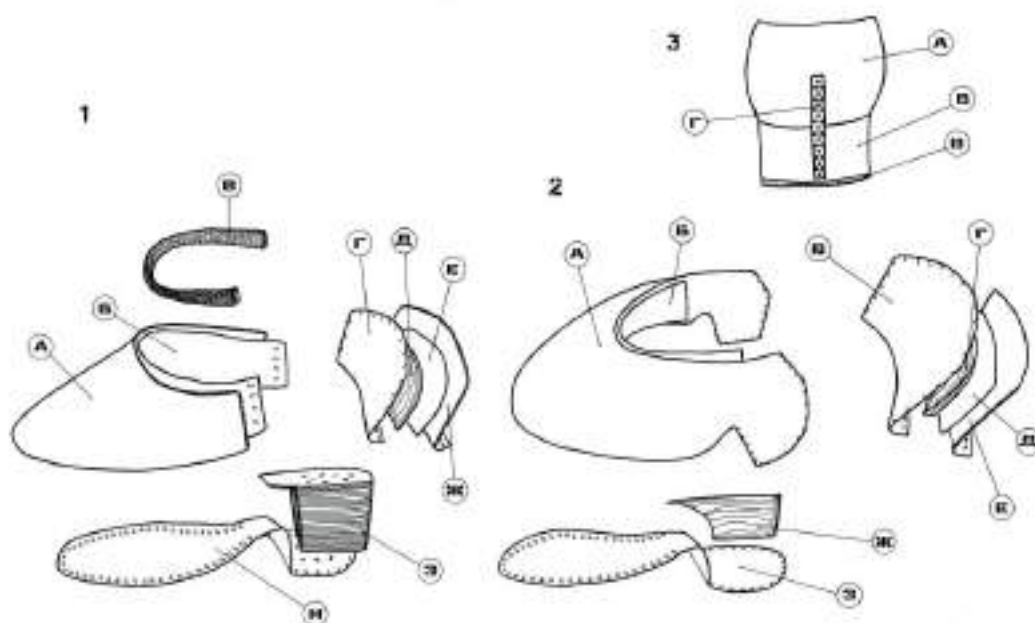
Схемы сборки башмаков. 1 – конструкция с наборным кожаным каблуком: А – головка; Б – поднаряд; В – тканая обшивка; Г – карман задника; Д – деревянный вкладыш; Е – кожаная прокладка; Ж – задник; З – наборный каблук; И – подошва. 2 – конструкция с деревянным каблуком: А – головка; Б – поднаряд; В – карман задника; Г – берестяной вкладыш; Д – кожаная прокладка; Е – задник; Ж – деревянный каблук; З – подошва. 3 – реконструкция башмаков, вид сзади: А – задник; Б – обтяжка деревянного каблука; В – подошва; Г – декоративная накладка
